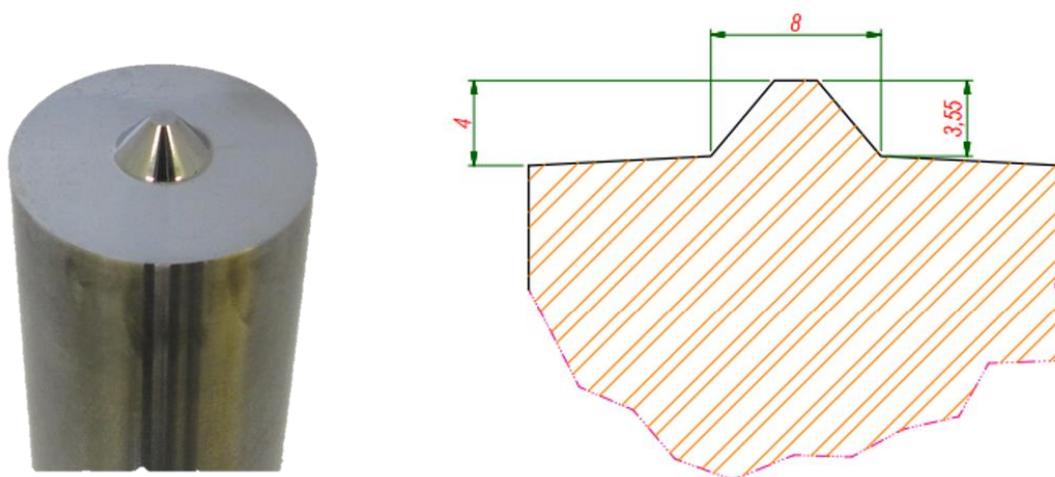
Primeira versão da ferramenta fabricada de WC-13%Co com o ombro e pino modificados para soldagem de chapas grossas.
